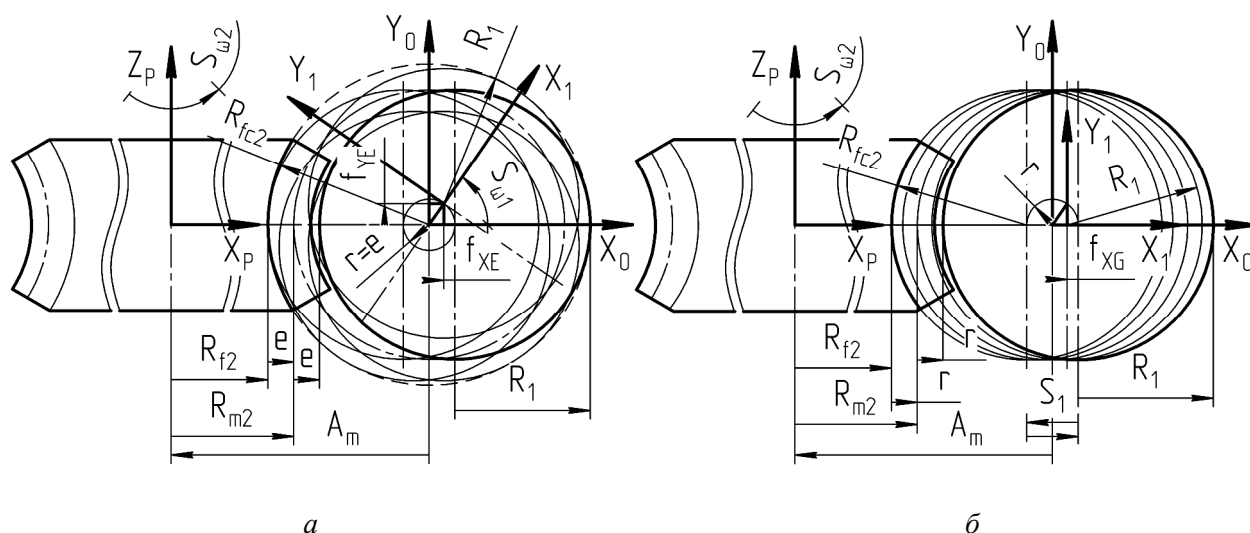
Нарізання зубців глобоїдного черв'ячного колеса способом колового руху дискової фрези (а) та способом зворотно-поступального руху дискової фрези (б)
